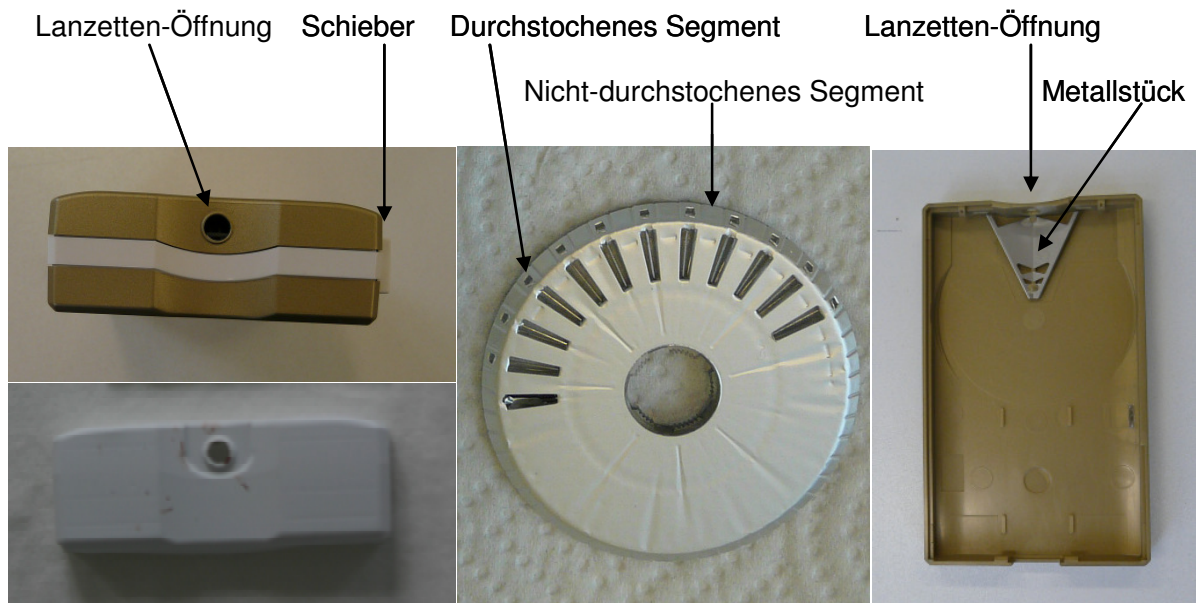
Aufsicht auf das Gerät und auf die Schutzkappe, Metalldisk mit Lanzetten (\varnothing 5,5 cm) und Innenansicht der rückenseitigen Gehäuseklappe (ca. 10 x 6 cm)
